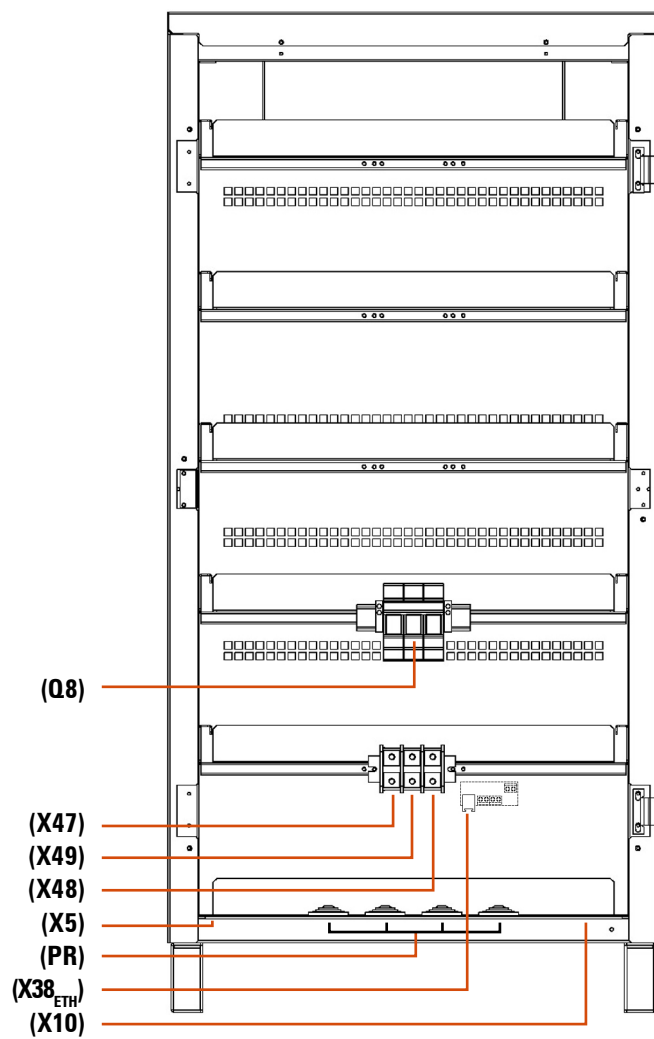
Vista frontal armario baterías N° 2, con puerta abierta.
